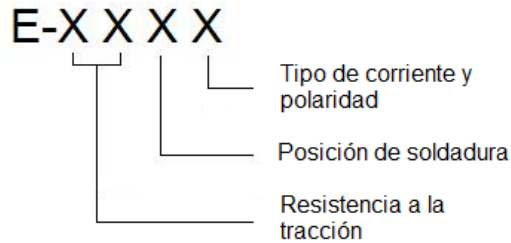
Nomenclatura de los electrodos para soldadura de arco
